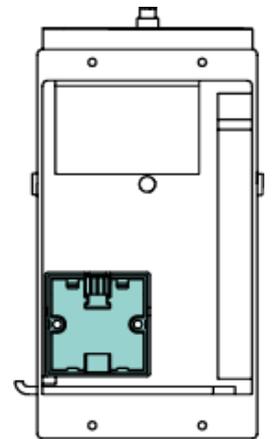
Croquis del interruptor - regulador de luz posicionado en la base
